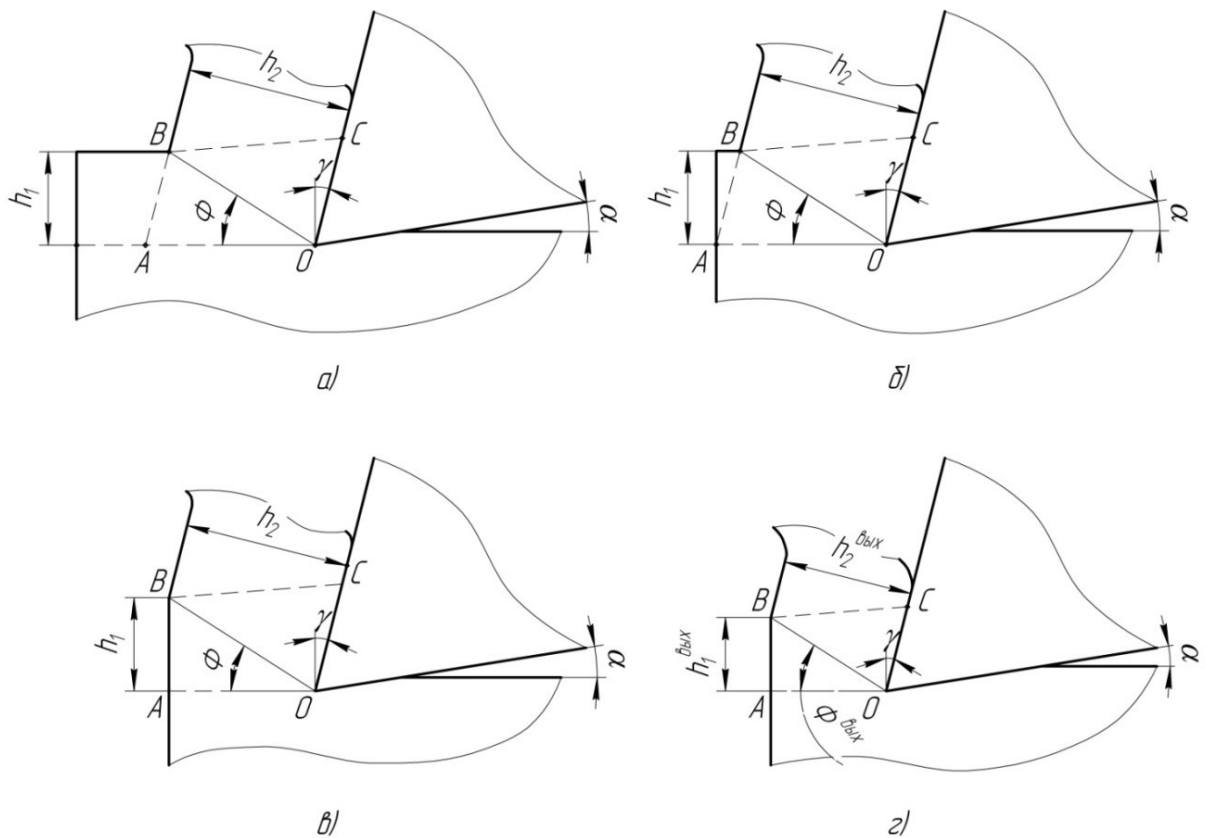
Схема резания с одной условной плоскостью сдвига:
